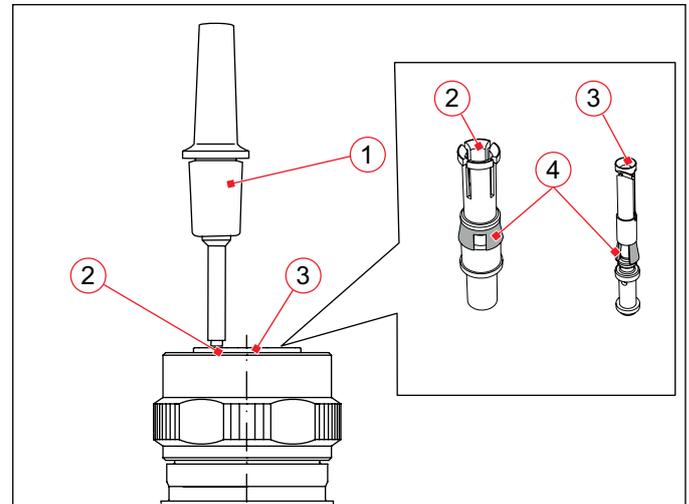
Demontage von Crimpkontakten (2,3) mit Ausdrückwerkzeug (1)
